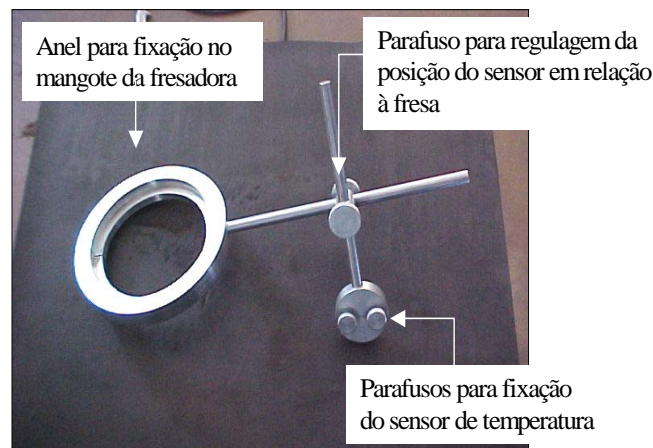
Dispositivo de fixação projetado e construído para os testes de medição da temperatura no fresamento.
